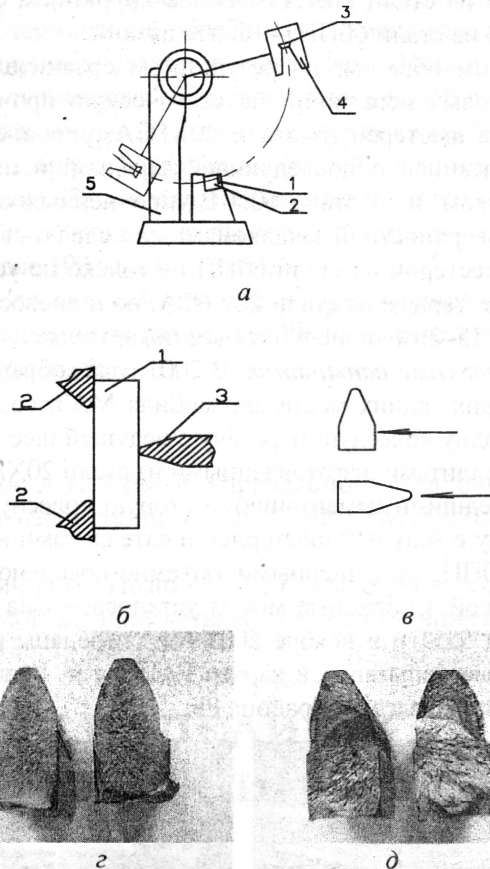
Схема испытаний зубьев шестерни колесной передачи автомобиля МАЗ на ударный изгиб — а-в и вид разрушенных при испытаниях образцов из стали 20ХНЗА — г; и 60ППГТ — д. 1 — испытываемый образец; 2 — опора; 3 — нож молота; 4 — молот копра; 5 — стойка
